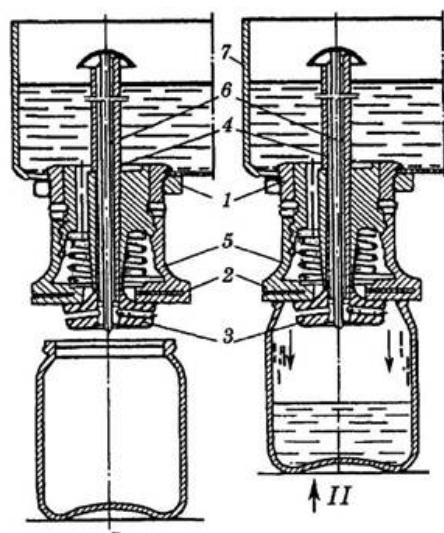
Пристрій для дозування за рівнем: 1 – гумовий патрубок; 2 – корпус; 3 – сидло-витискувач; 4 – утримувач; 5 – пружина; 6 – трубка; 7 – резервуар
